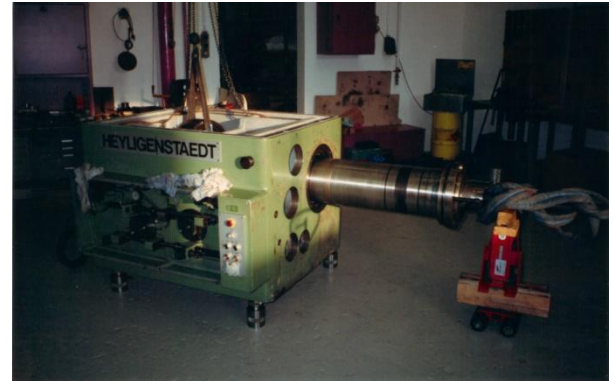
Ein äusserst gut konstruiertes Getriebe einer Drehmaschine.
